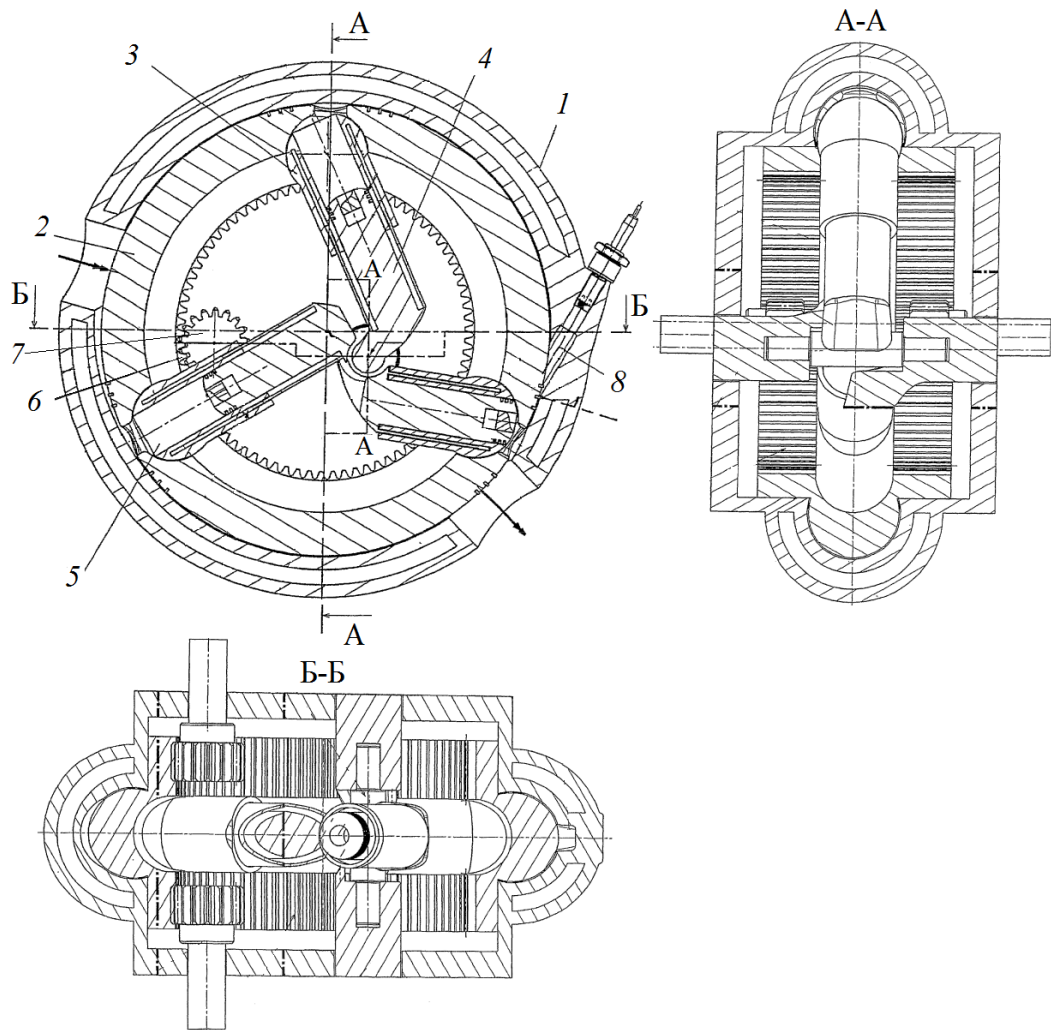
Загальна будова роторно-поршневого двигуна внутрішнього згоряння [124]: 1 – корпус двигуна; 2 – ротор; 3 – робочий циліндр; 4 – поршень; 5 – робоча камера циліндра; 6 – зубчастий вінець; 7 – вихідний вал; 8 – камера згоряння
